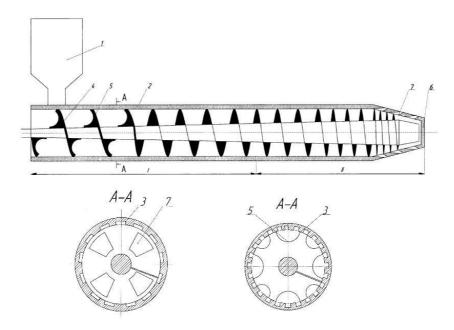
Пресс-экстредер по патенту РФ 2622163 [25]: 1 – загрузочный бункер; 2 – корпус; 3 – профилированная внутренняя поверхность; 4 – шнек; 5 – вырез; 6 – коническая матрица; 7 – отверстие
